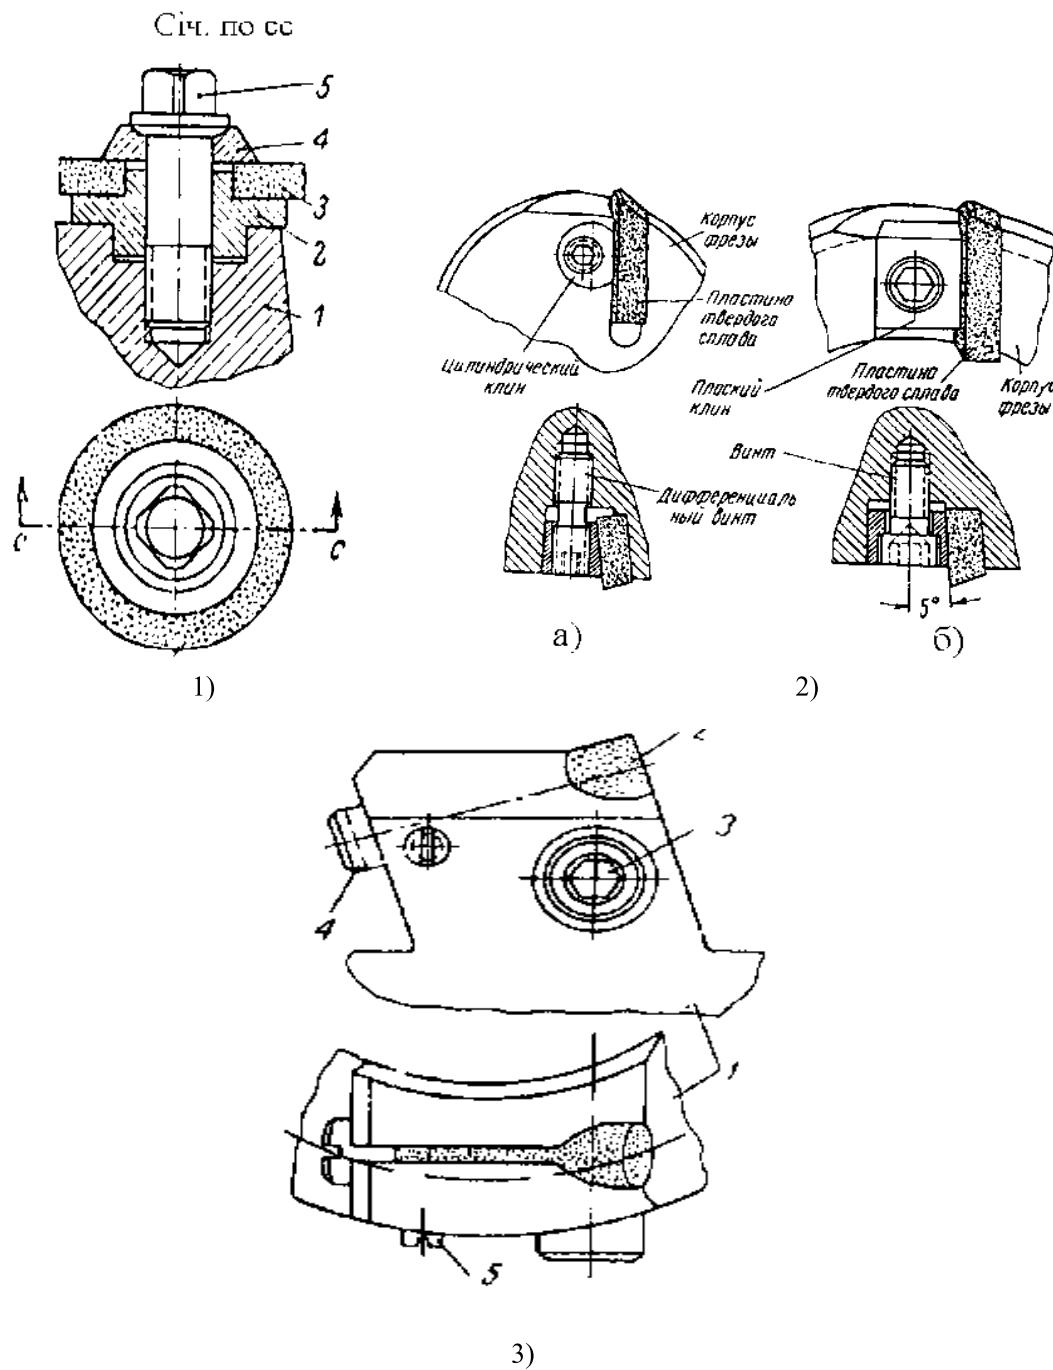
Вузол механічного кріплення різального ножа: 1 - твердосплавного диску (1 – корпус фрези; 2 – шайба упорна; 3 – твердосплавний диск; 4 – сферична шайба; 5 – кріпильний гвинт); 2 - призматичних пластин твердого сплаву (а – кріплення циліндричним клином і диференційним гвинтом; б – кріплення плоским клином і гвинтом); 3 - циліндричного стовпчика (1 – корпус фрези; 2 – твердосплавний циліндричний стовпчик; 3 – кріпильний гвинт; 4 – упорний гвинт; 5 – стопорний гвинт)
